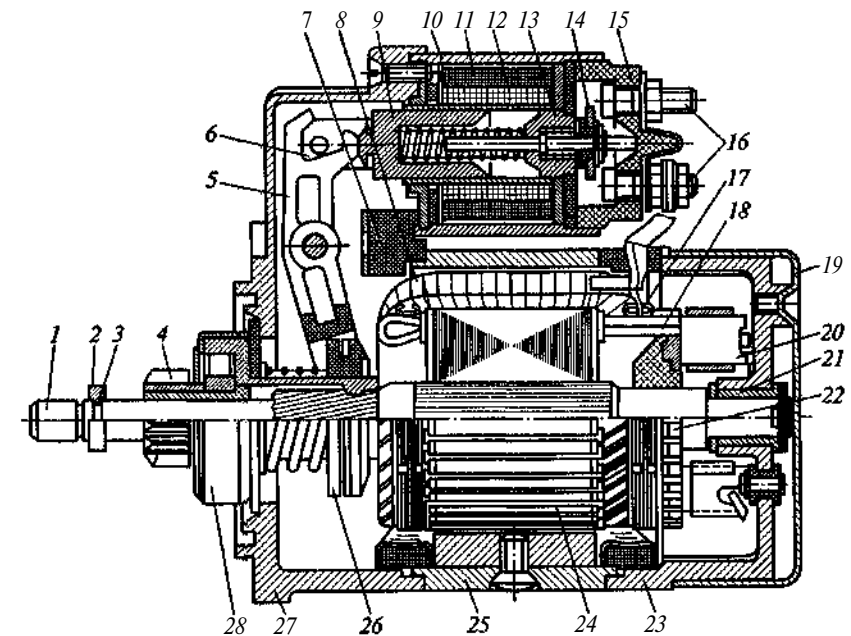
Электростартер с торцевым расположением щеток: 1 — вал якоря; 2 и 3 — соответственно замковое и упорное кольца; 4 — шестерня; 5 — рычаг привода; 6 — тяга реле; 7 — заглушка; 8 — обмотка возбуждения; 9 — якорь тягового реле; 10 и 15 — корпус и крышка тягового реле; 11 и 12 — удерживающая и втягивающая обмотки; 13 — сердечник втягивающего реле; 14 — подвижный контакт; 16 — контактные болты; 17 — бандаж обмотки якоря; 18 — обмотка якоря; 19 — защитный кожух; 20 — щетка; 21 — подшипник скольжения; 22 — торцевой коллектор; 23 — коллекторная крышка; 24 — якорь стартера; 25 — корпус; 26 — поводковая муфта; 27 — передняя крышка; 28 — роликовая муфта свободного хода
